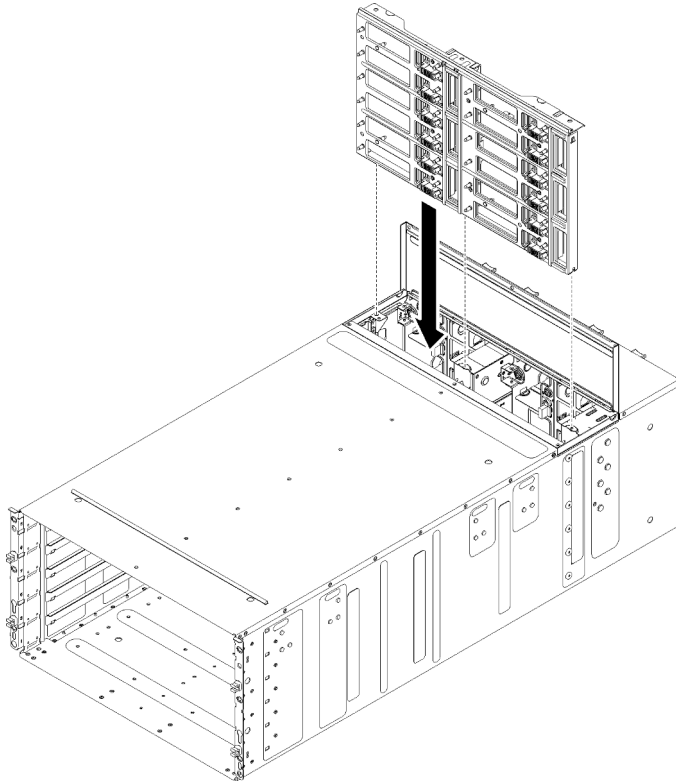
Installieren der Mittelplatte des Gehäuses
